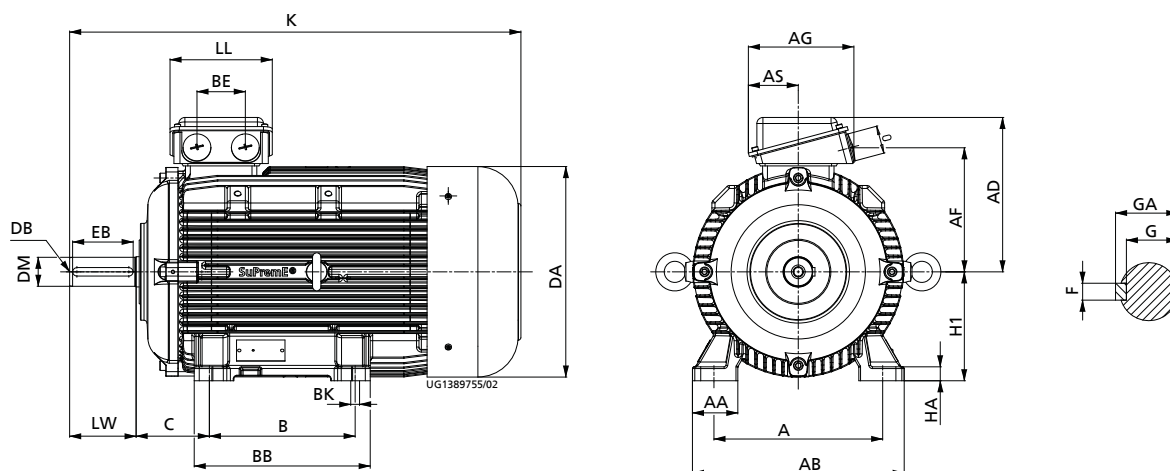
Исполнение со стандартной крышкой подшипника (B3,...)
